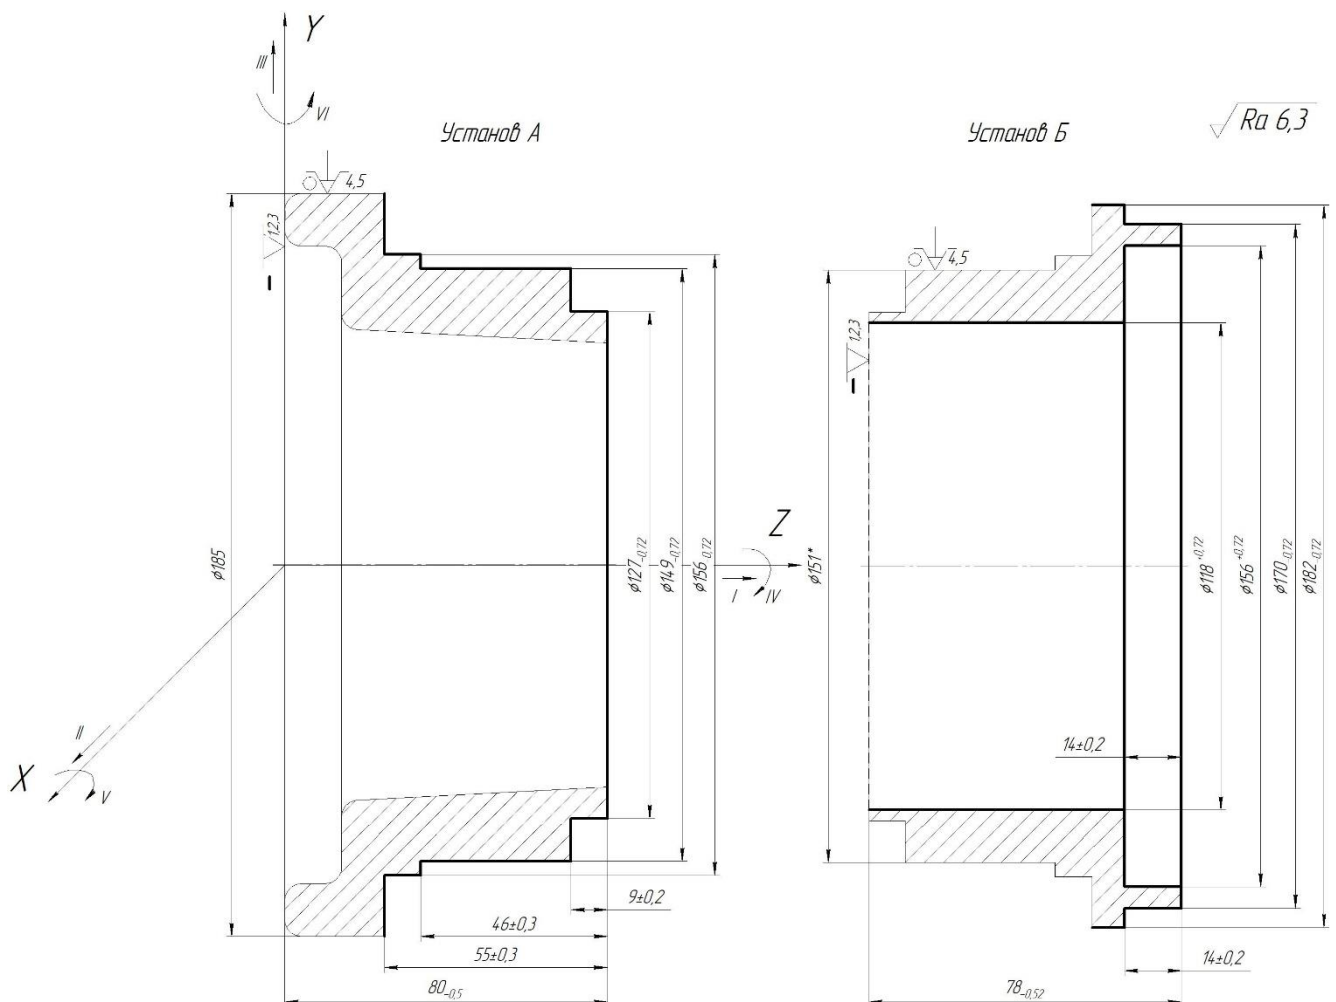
Схема установки заготовки на токарній операції (варіант 2)
